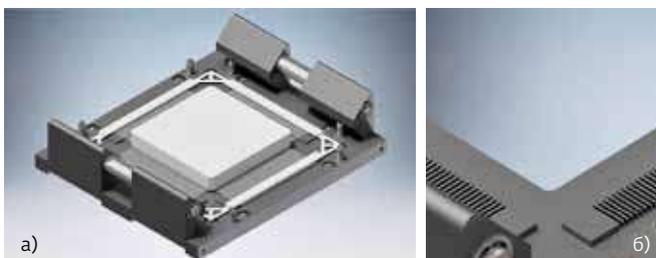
КУ для корпусов с керамической рамкой: а – общий вид; б – увеличенный вид
